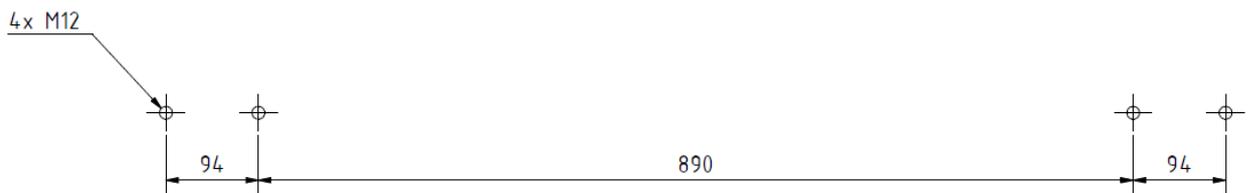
Bohrbild zur Befestigung der Motorfangvorrichtungen mit der Standard Motorwelle (1.000 mm)
